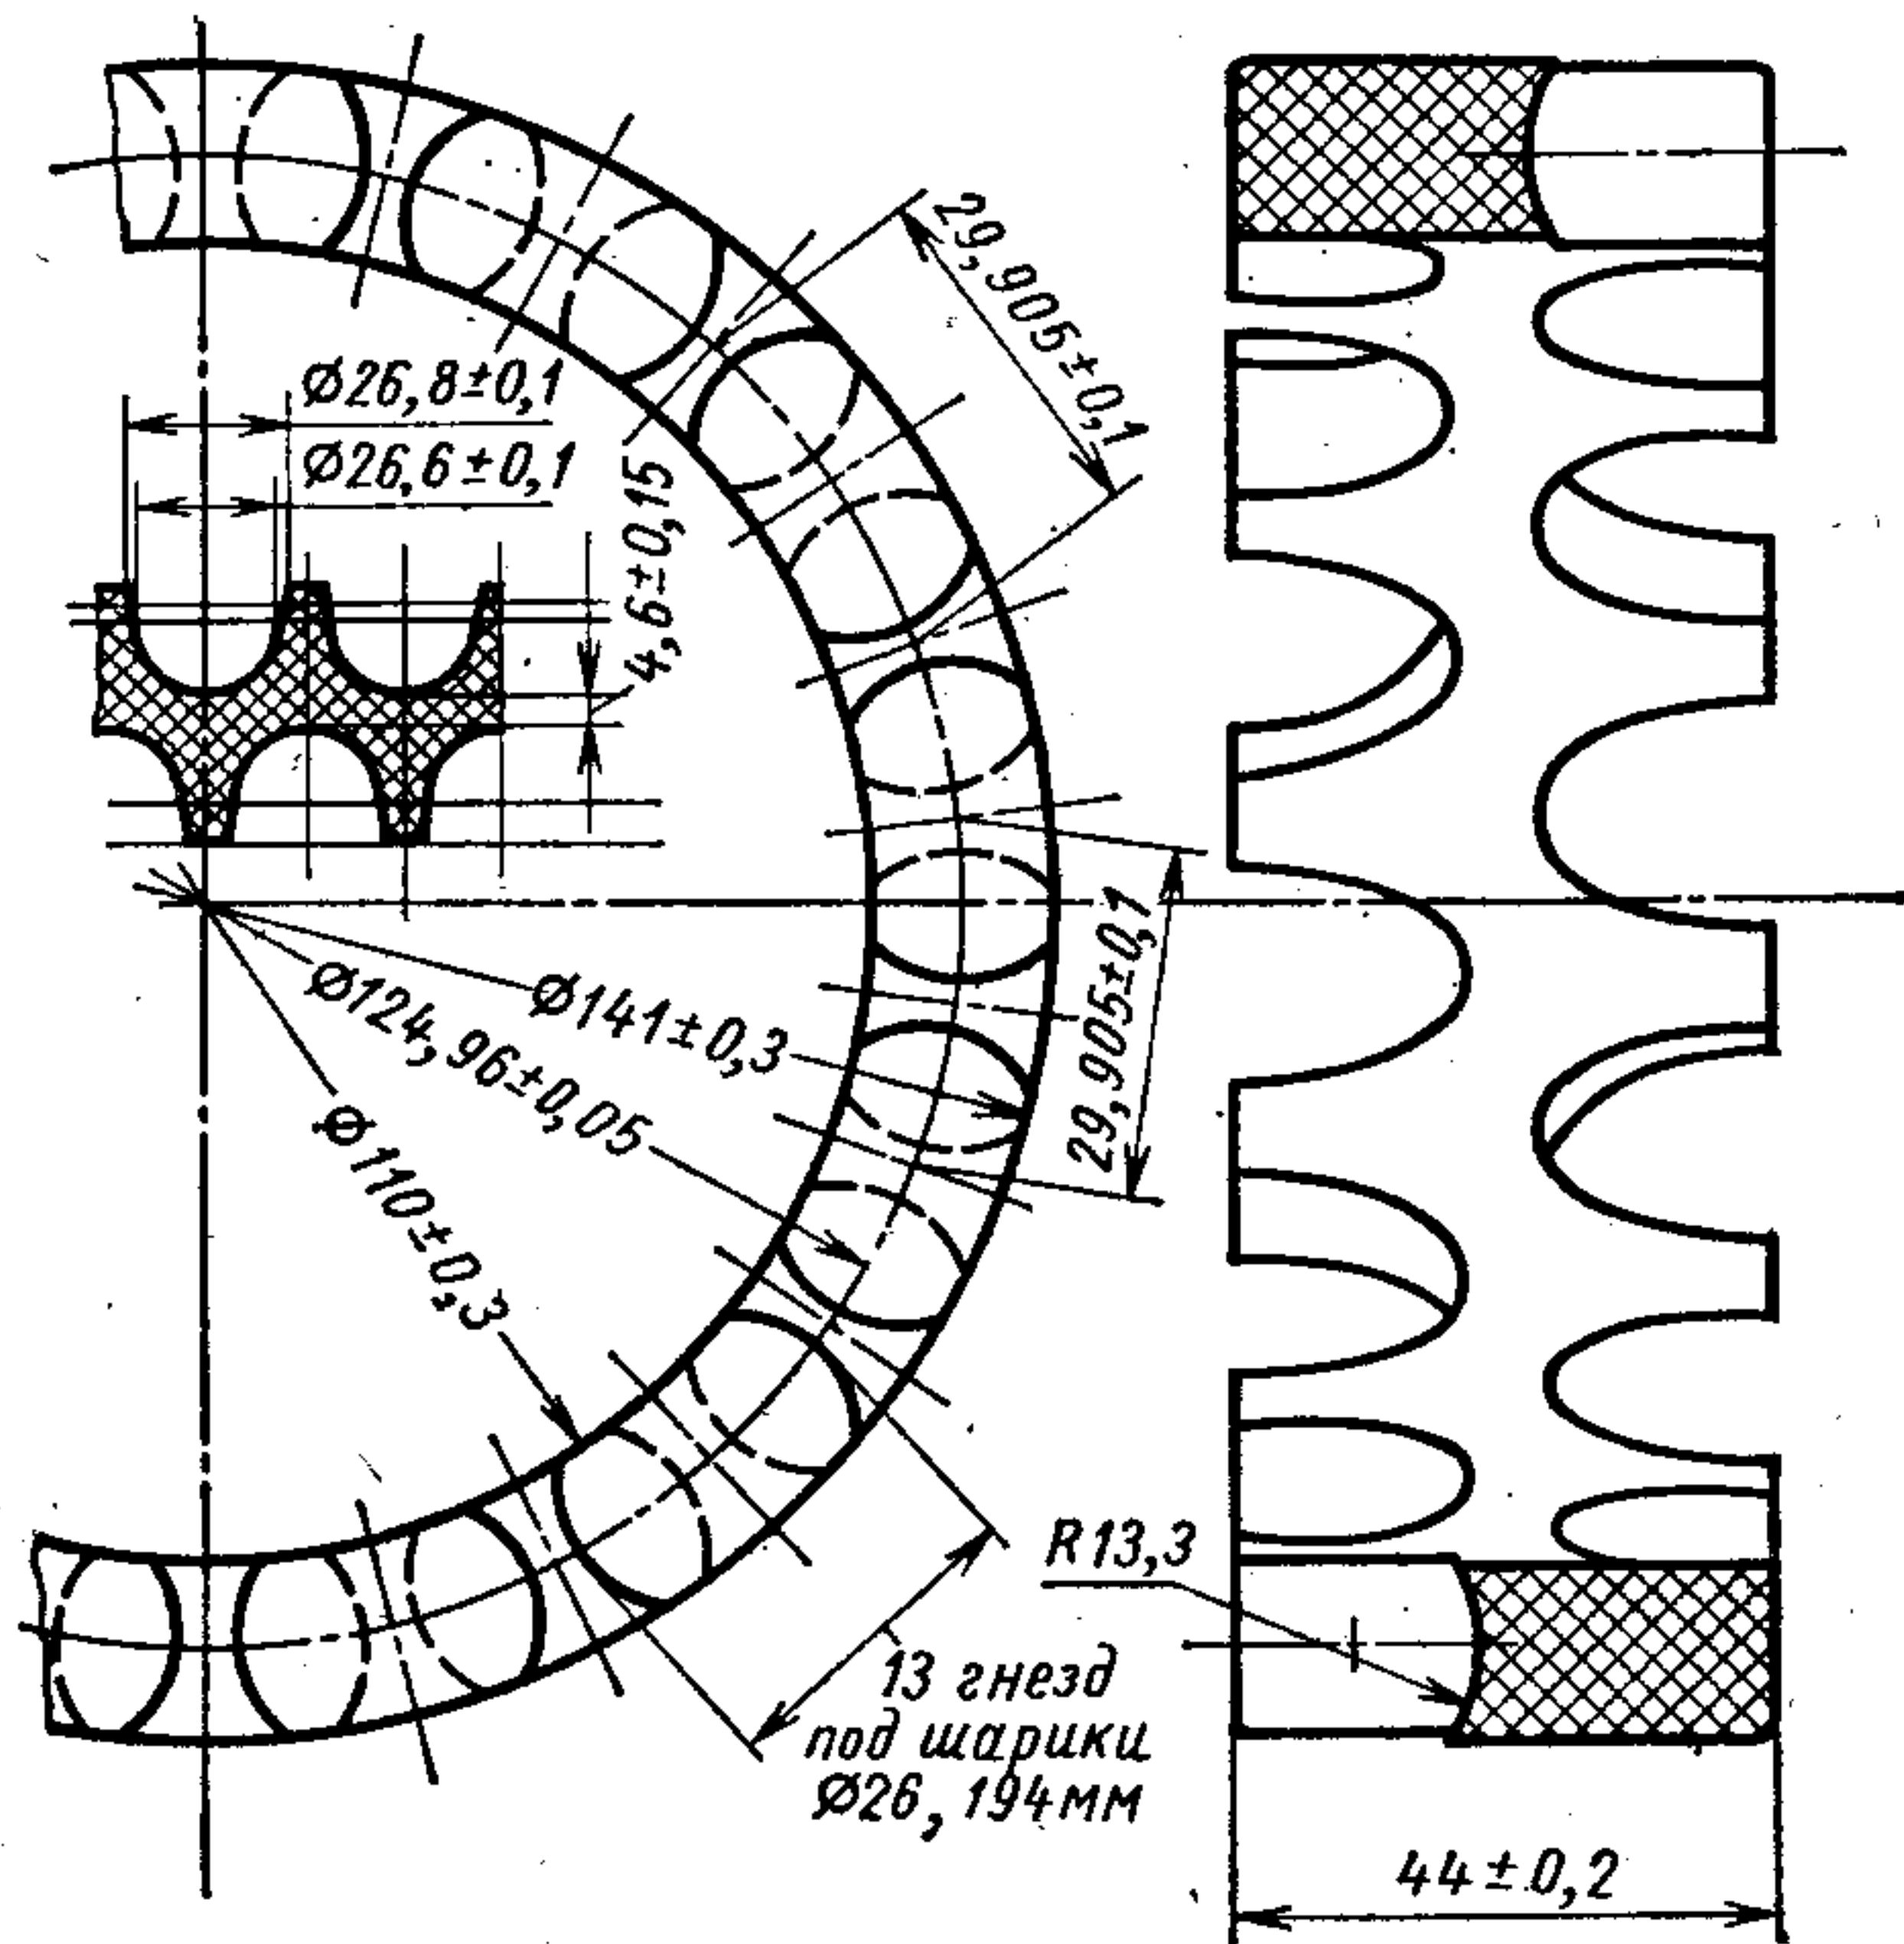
Сепаратор двухрядного роликоподшипника из волокнита
